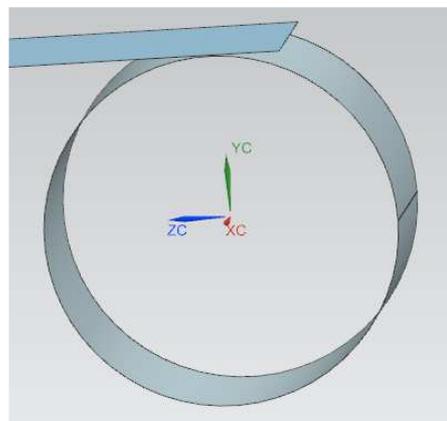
Расположение листовой заготовки относительно правого нижнего вала
